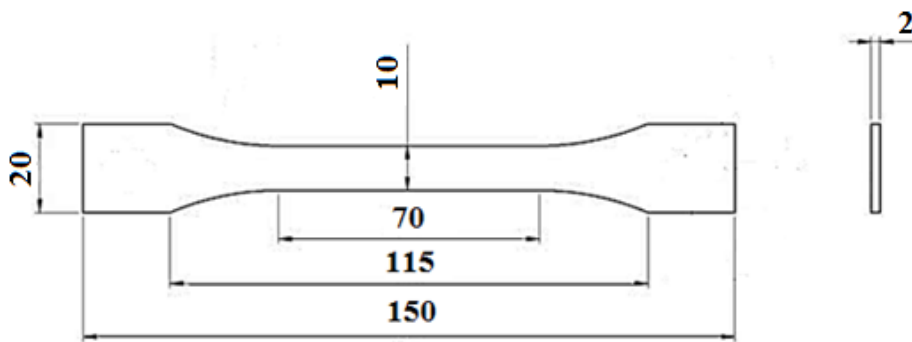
Geometria e dimensões dos provetes de adesivo utilizados no ensaio de tração.
